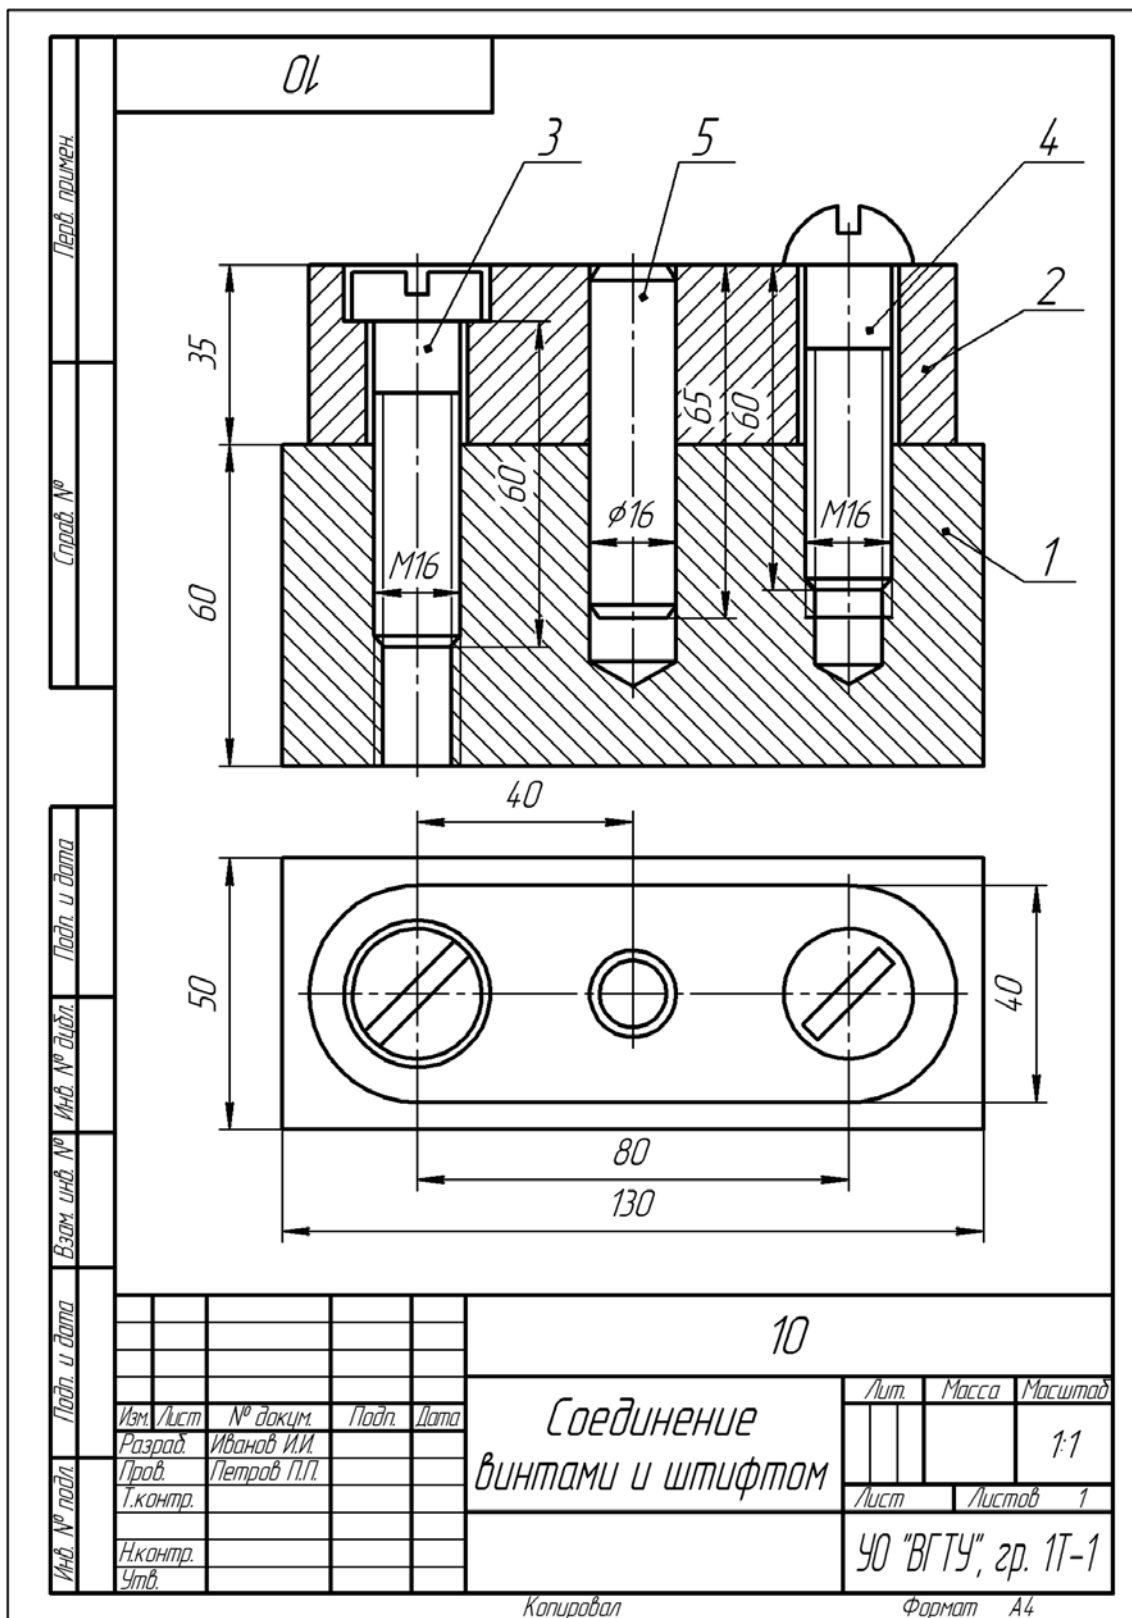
Сборочный чертеж «Соединение винтами и штифтом»
